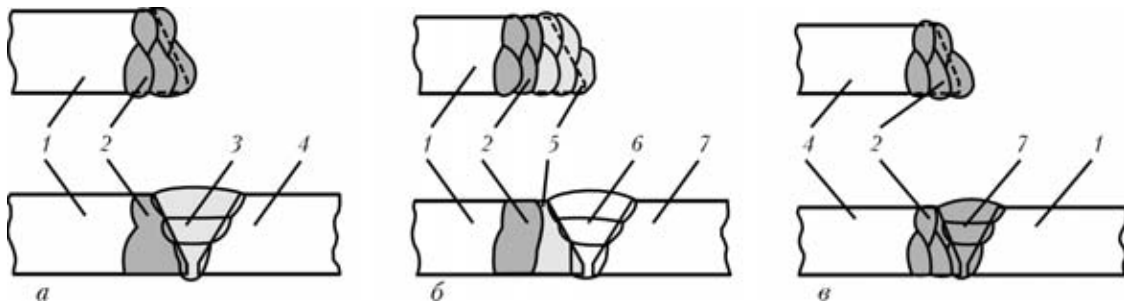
Схемы первого (а), второго (б) и третьего (в) технологических вариантов сварных соединений разнородных сталей: 1 — основной металл (сталь 20); 2 — наплавка армко-железа; 3 — шов, сваренный с применением присадочного металла Св-10Х16Н25АМ6; 4 — основной металл (сталь 08Х18Н10Т); 5 — наплавка присадочного металла Св-10Х16Н25АМ6; 6 — шов, сваренный с применением присадочного металла Св-04Х19Н11М3; 7 — шов, сваренный с применением армко-железа в качестве присадочного металла
